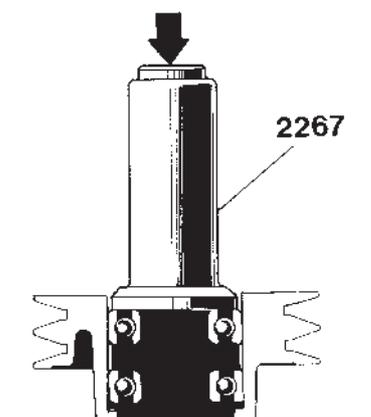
Montage des roulements avant et arrière dans la poulie.
